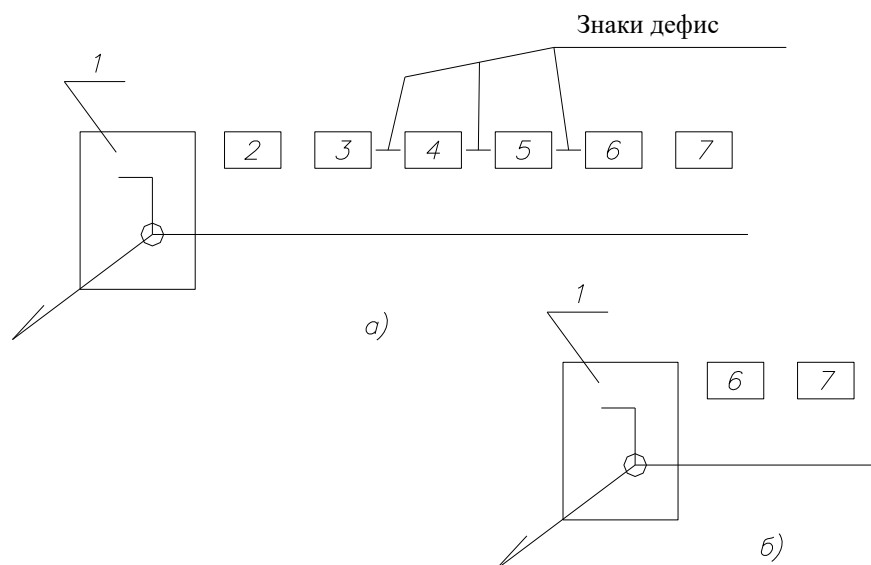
Структура условного обозначения сварного шва
